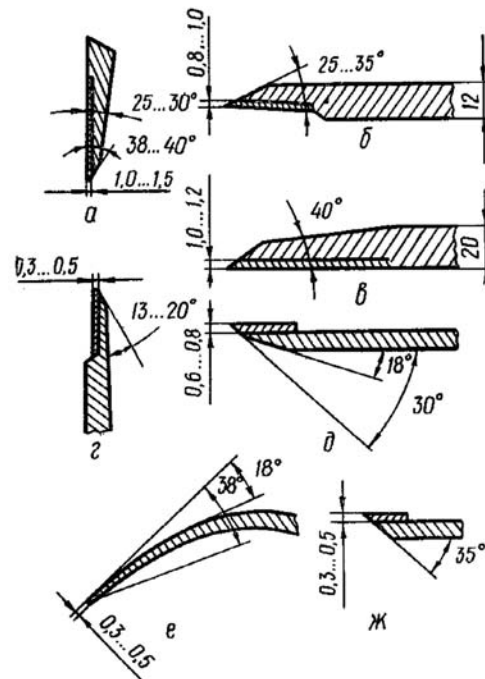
Геометрия заточки лезвий: а — лемеха плуга; б — лемеха плоскореза; в — долота плоскореза; г — лап культиватора; д — диска тяжелой бороны; е — диска лулильника; ж — фрезы почвообрабатывающей
